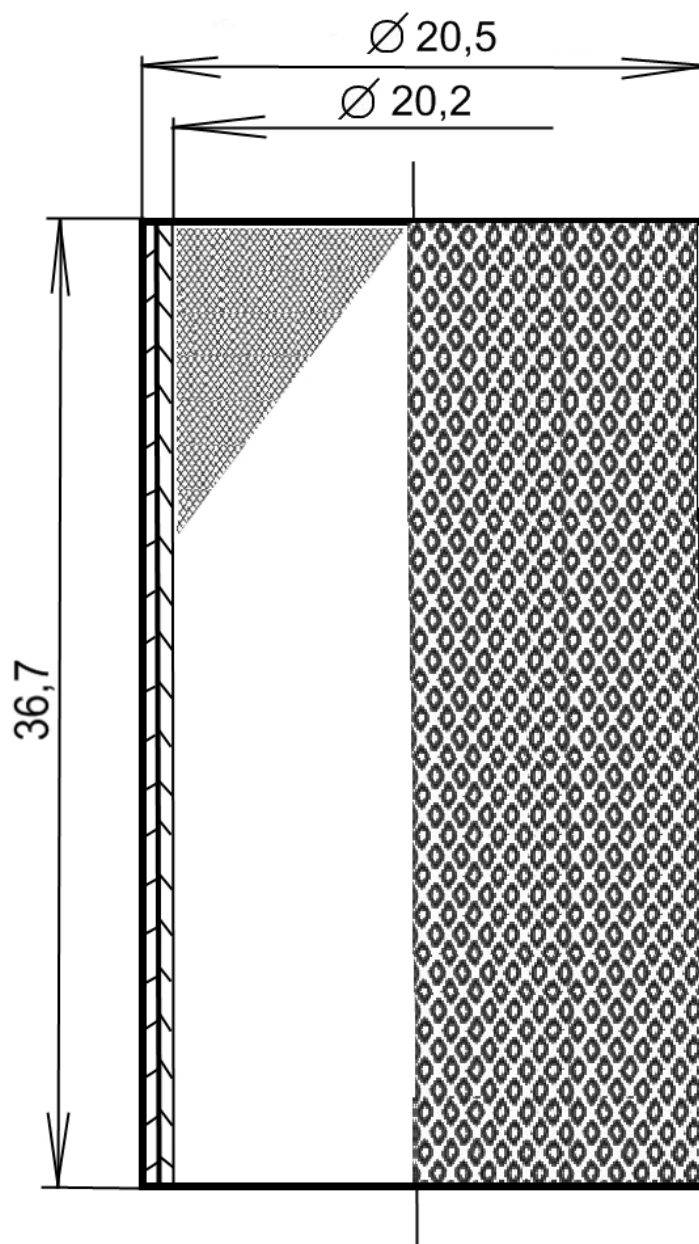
Габаритные размеры фильтрующего элемента.
